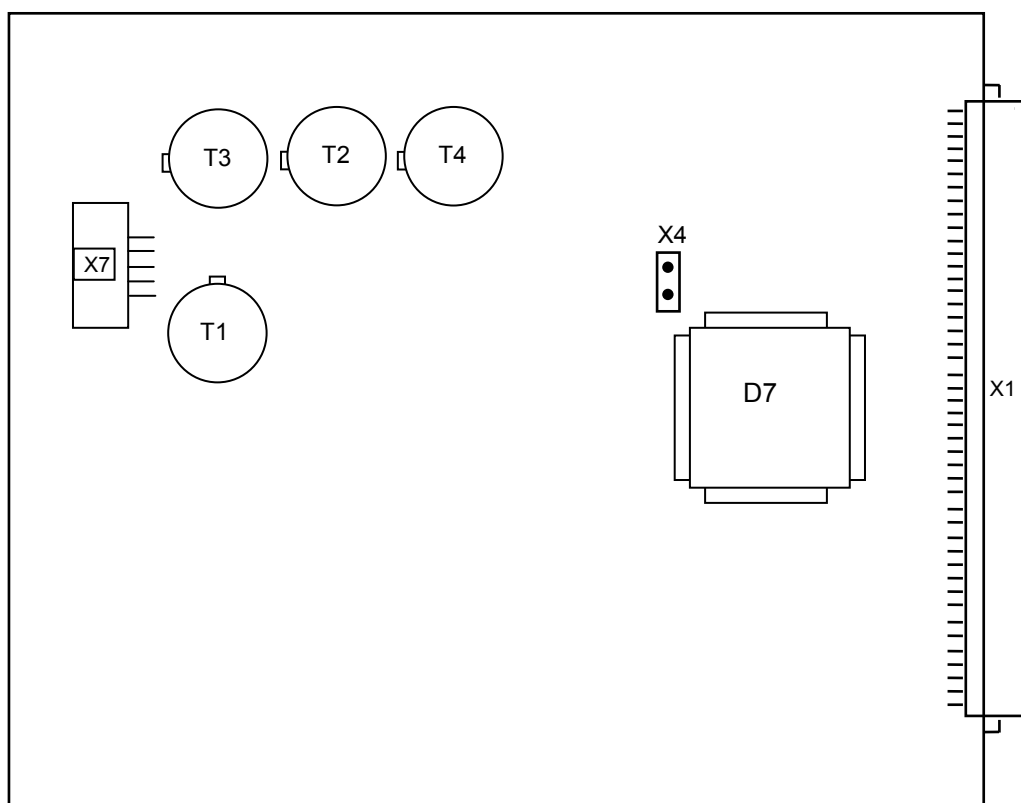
Расположение соединителей штыревых на печатной плате ячейки ОЦС
